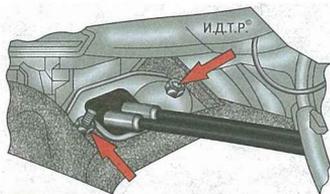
Крепление уплотнителя тросов управления коробкой передач
